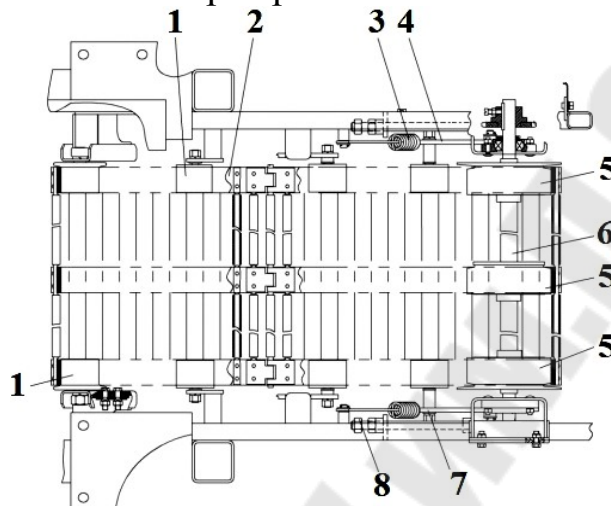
Второй сепарирующий элеватор: 1 – ролики поддерживающие; 2 – ремень; 3 – пружина; 4, 7 – кронштейны; 5 – колеса ведущие; 6 – вал приводной; 8 – шпилька
